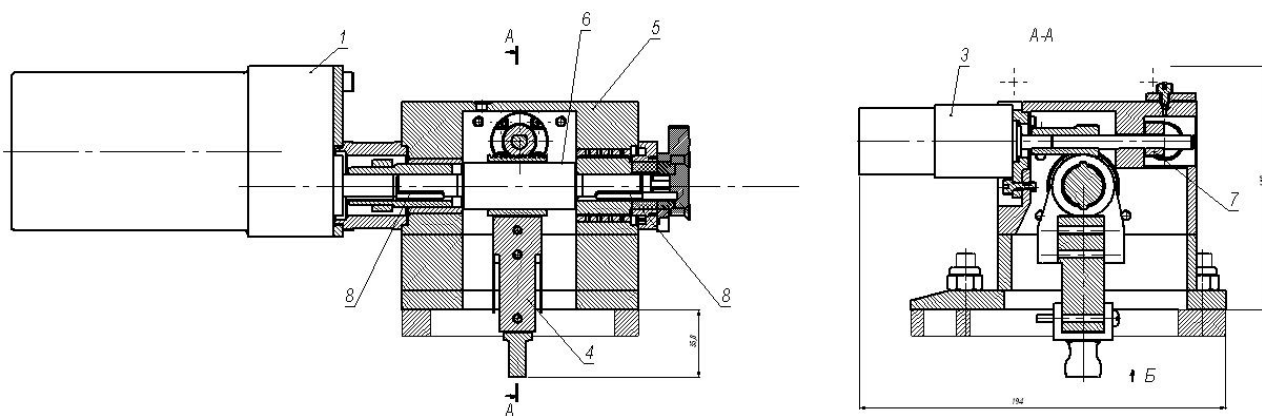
Будова виконавчого пристрою механізму керування коробкою передач
